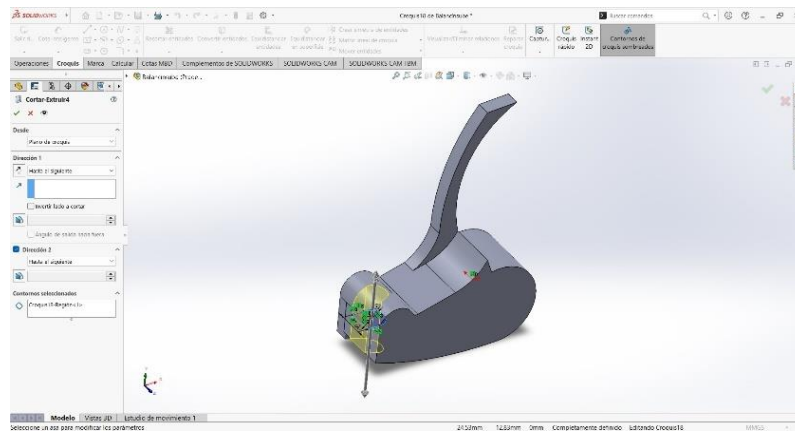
Balancín 1 (Extrusionado de corte de Croquis 5). Fuente: SolidWorks
